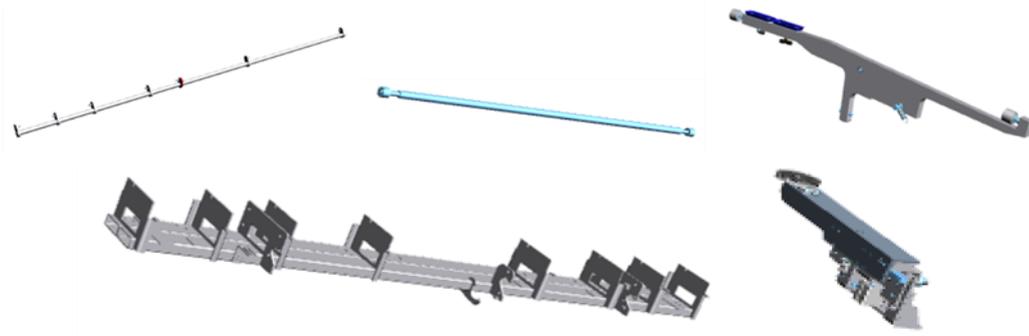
Componenti del ponte di attestatura e specifica del meccanismo del gruppo rotatore.
